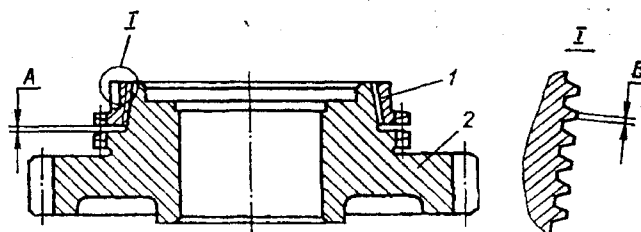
Замер зазора между торцами венца шестерни и кольцом синхронизатора: 1 – кольцо синхронизатора; 2 – шестерня; А – зазор в новых шестернях равен 1,325...2,085 мм, в работавших деталях – не менее 0,8 мм; В – ширина резьбы на вершине в кольце синхронизатора новой детали 0,06...0,1 мм; в работавшей – не более 0,3 мм
